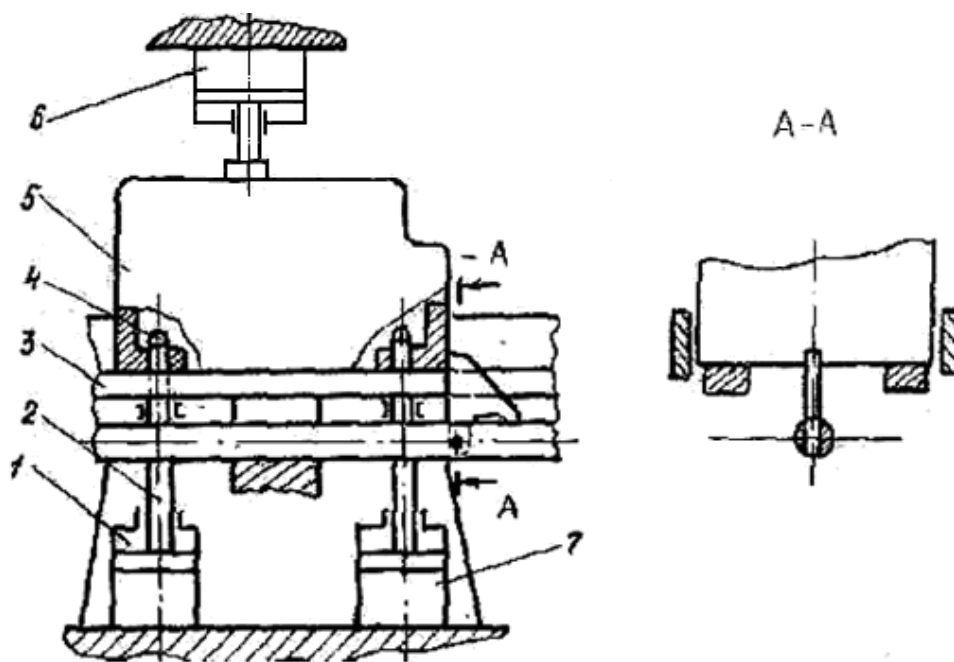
Приспособление - спутник для автоматической линии
